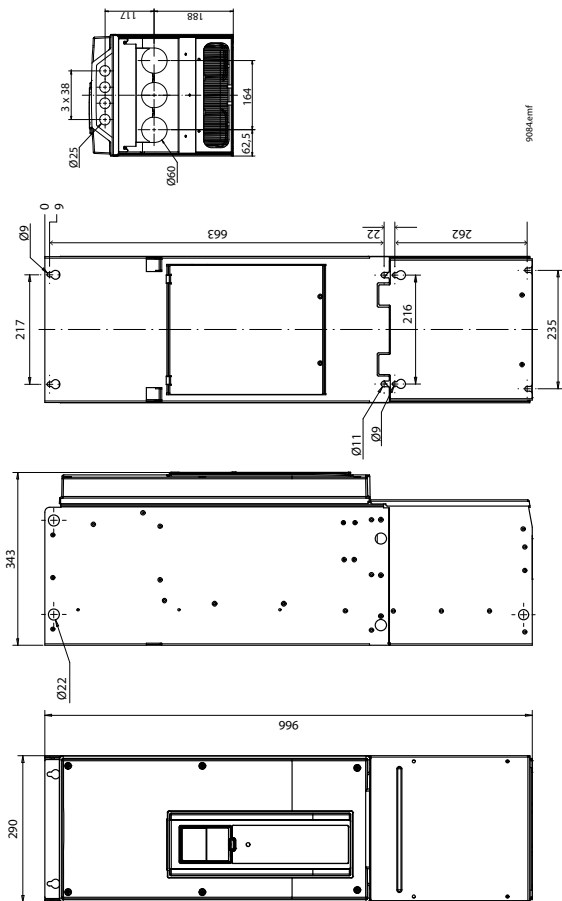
Dimensões do inversor de CA Praxi, MR8 IP21 e IP54
